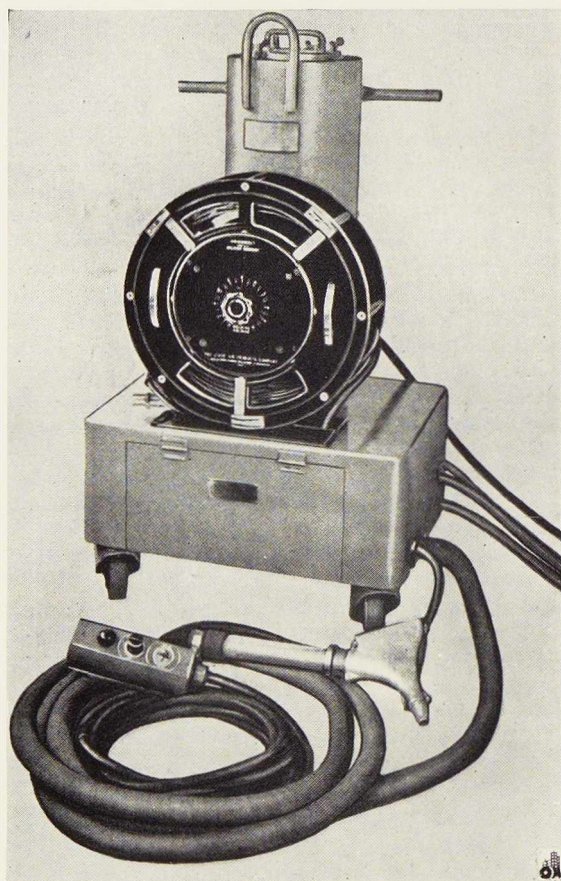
Appareil semi-automatique pour le soudage par le procédé Unionmelt.
